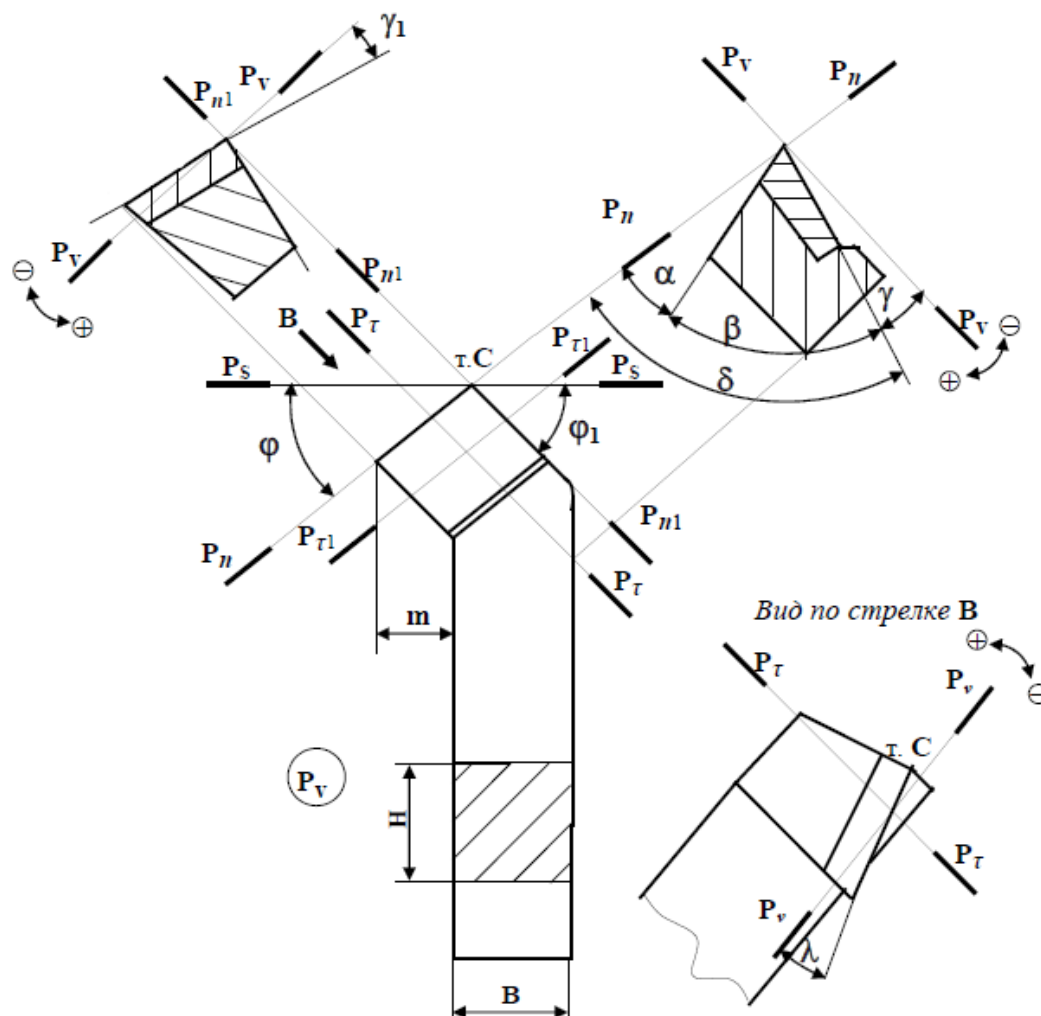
Эскиз проходного резца с отогнутой головкой
